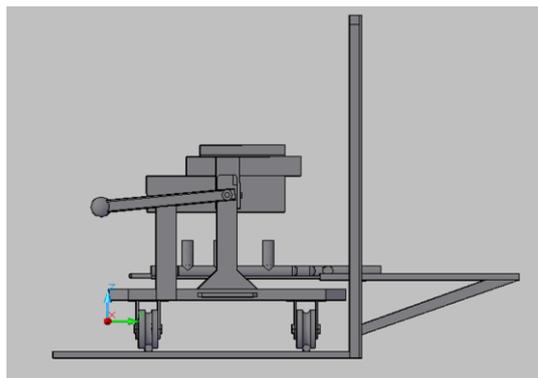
Diseño de base de molde y quemador en Auto Cad (vista sw).
